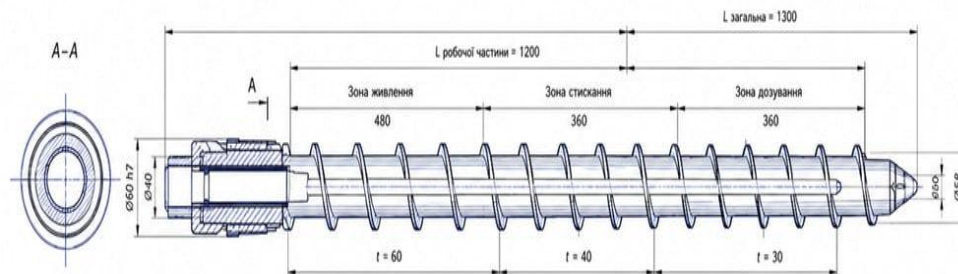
Конструктивна схема модернізованого пластикаційного механізму
